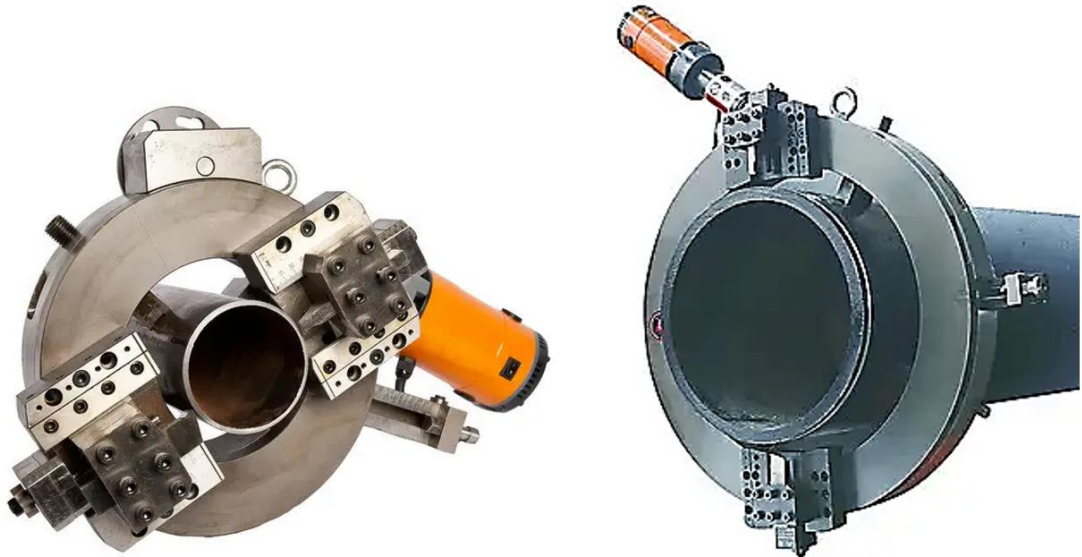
Загальний вигляд роз'ємного труборізу TP(ISC)-300 [24]
